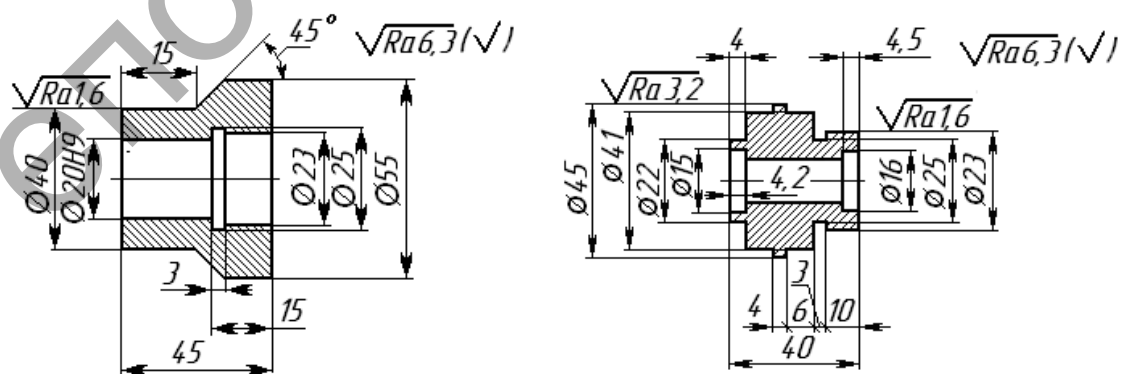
Типовые детали, обрабатываемые на токарно-револьверных станках
